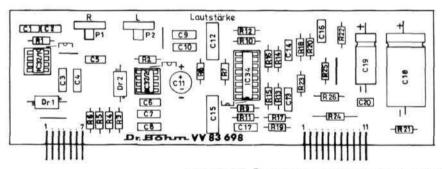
Positionsnummernplan Lautstärke-Modul Platine VV 83 698
